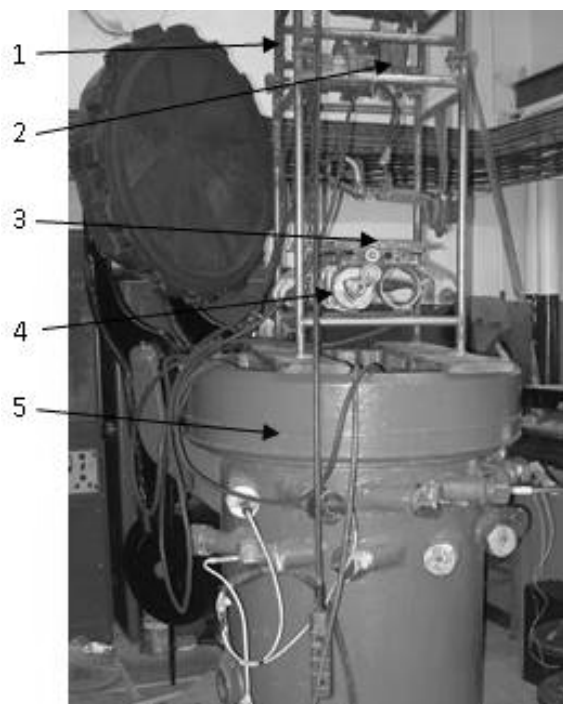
Автомат для подводной сварки перед испытаниями в барокамере:
